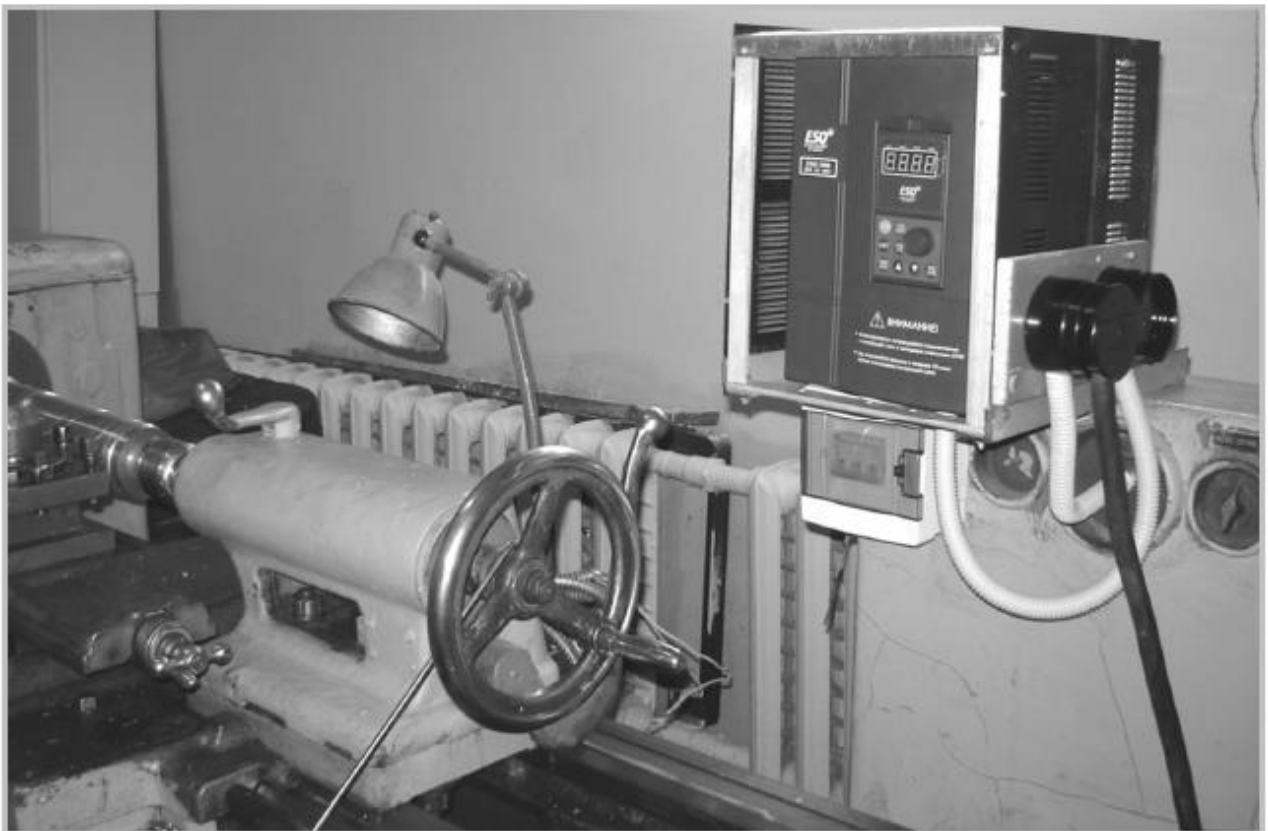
Загальний вигляд експериментальної установки на базі токарно-гвинторізного верстата 1К62
